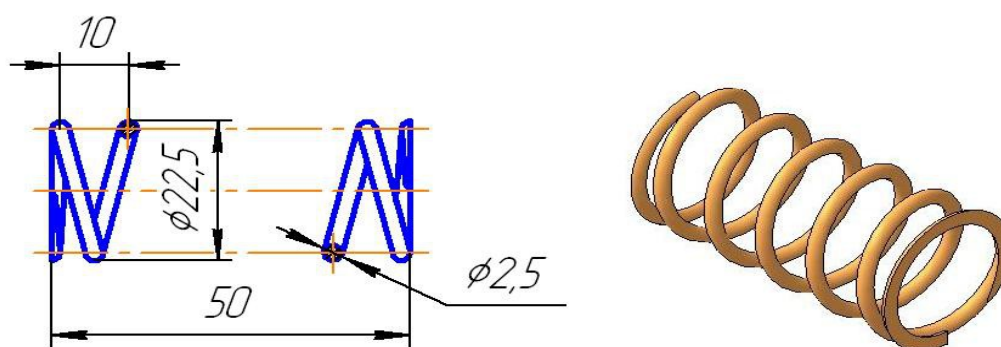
Чертеж и модель детали «*Пружина сжатия*»
